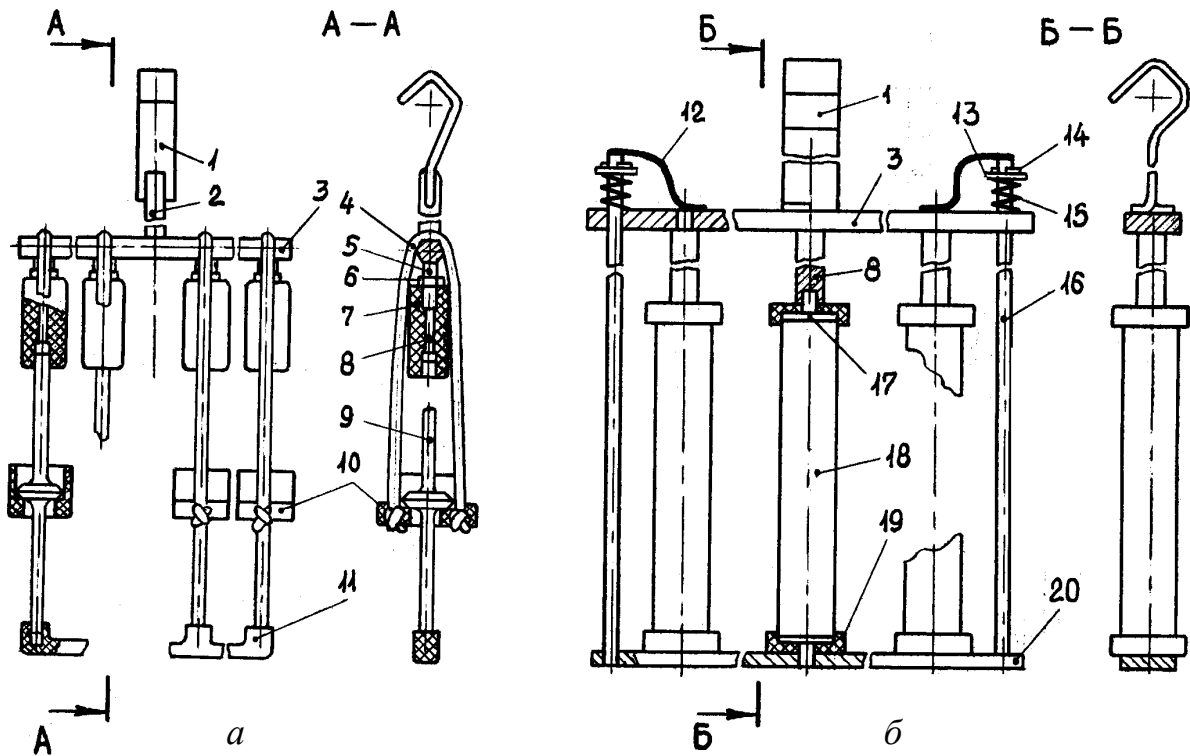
Групповые подвески для наращивания гальванических покрытий на: *а* – стержни клапанов; *б* – шкворни. 1 – контактный крючок; 2 – удлинитель крючка; 3, 20 – траверса (верхняя, нижняя); 4 – стяжное кольцо (резина); 5 – переходник (сталь); 6 – гайка; 7 – втулка текстолитовая; 8 – контактный стержень; 9 – клапан; 10 – кожух экранирующий; 11 – траверса изоляционная; 12 – провод гибкий; 13 – шайба; 14 – шплинт; 15 – пружина; 16 – стержень стяжной; 17 – контактный наконечник; 18 – шкворень; 19 – шайба изоляционная
